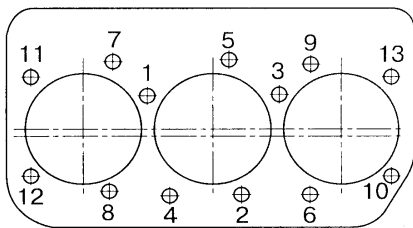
Схема затяжки болтов головок цилиндров двигателя
